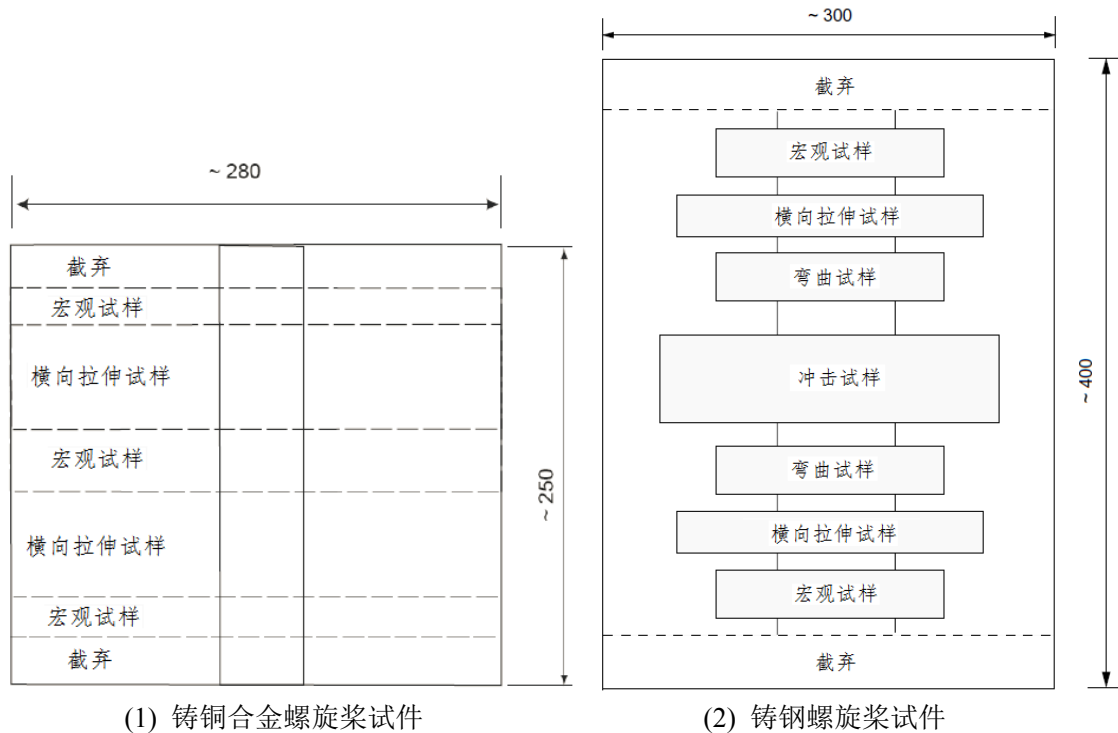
螺旋桨修补焊接工艺认可试件取样位置
